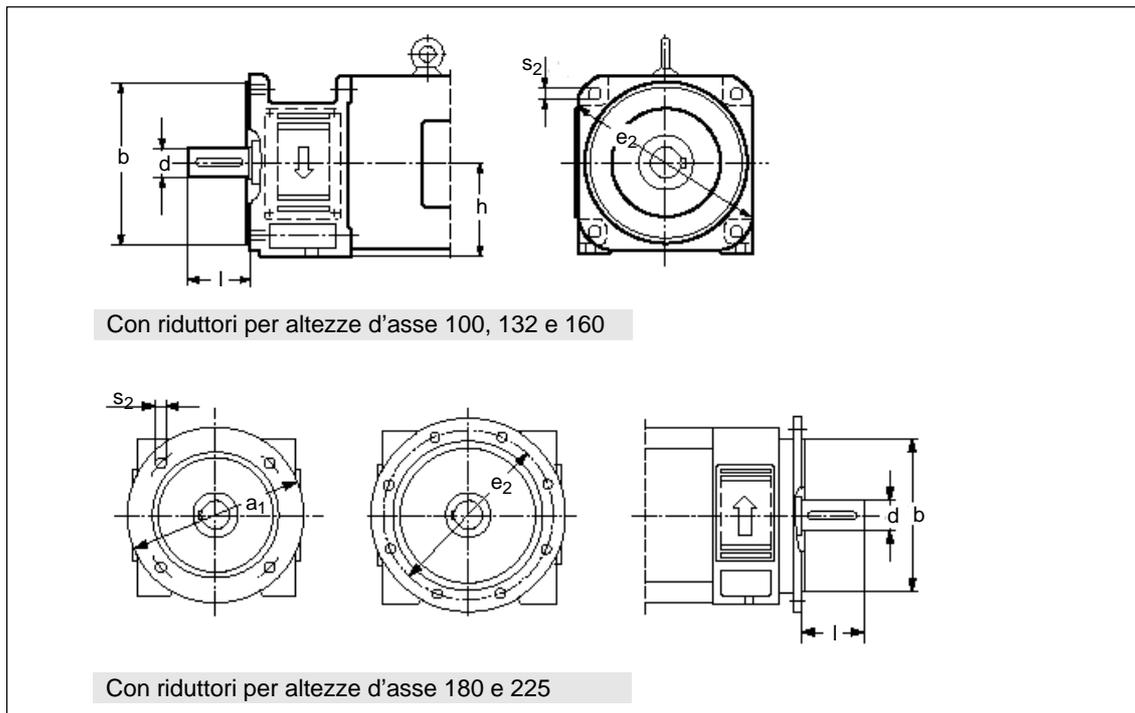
Dimensioni delle flange per motori in corrente trifase (per le dimensioni vedere la tabella 3-6)
